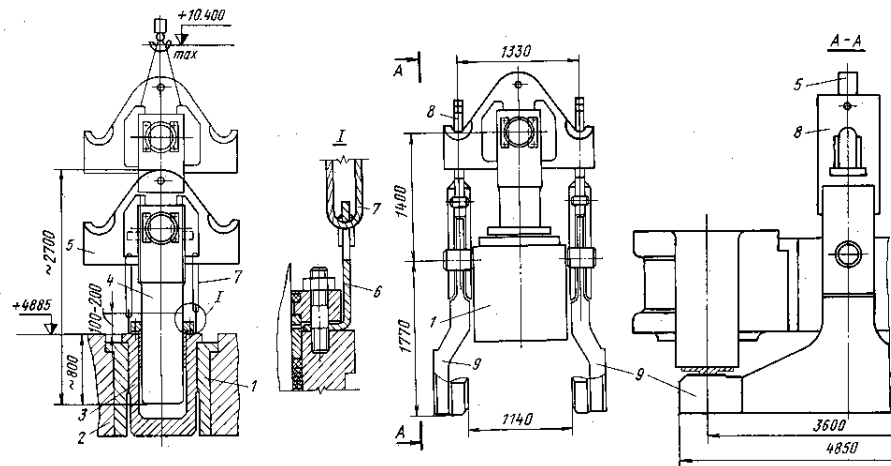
Схема монтажу врівноваження верхнього опорного вака
